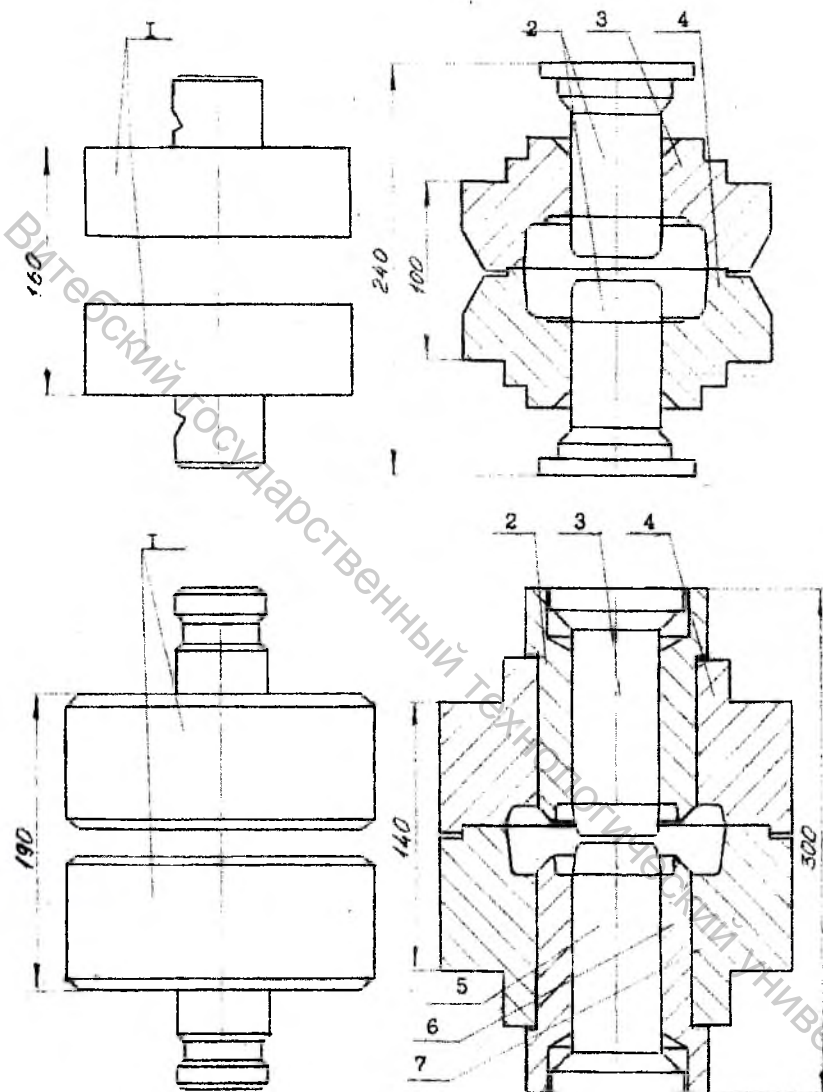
Рабочие части штампов для двусторонней безоблойной штамповки
